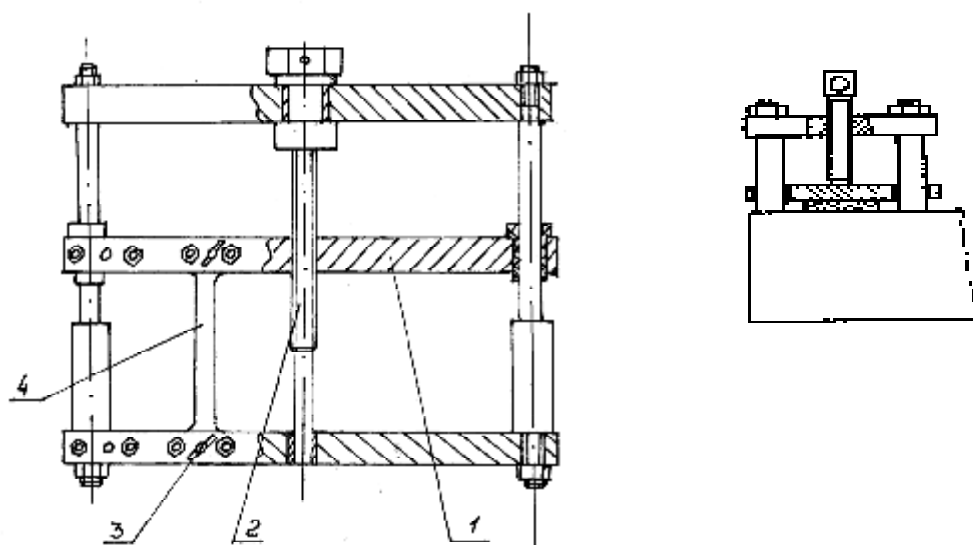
Конструктивная схема приспособления для одноосного растяжения: а - разрез зажима образца; б - общий вид приспособления (планка; 2 - винт; 3 - зажимы; 4 – образец)
